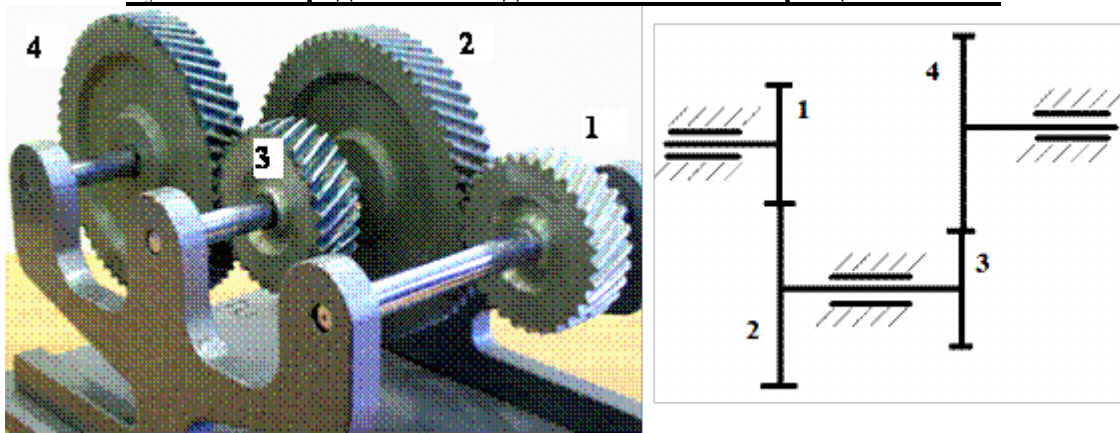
Двухступенчатая зубчатая передача и ее кинематическая схема
